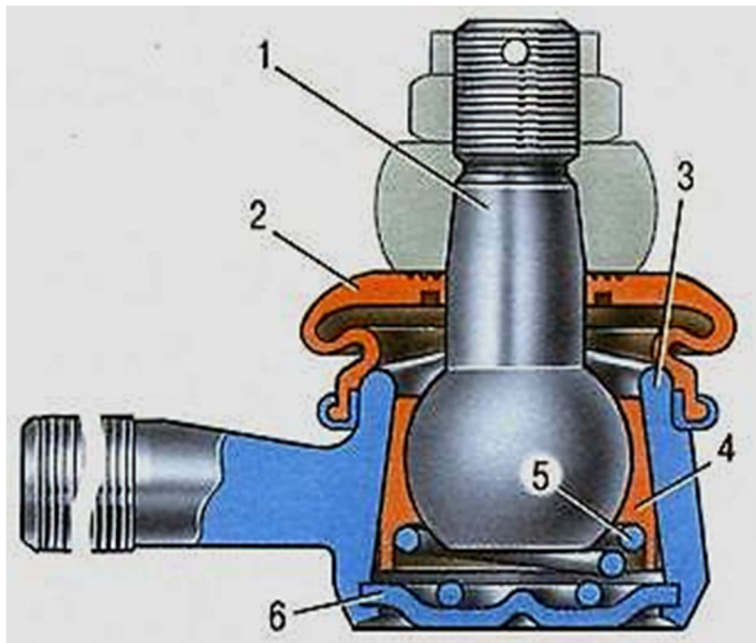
Схема кульового шарніра рульової тяги ВАЗ-2106:
